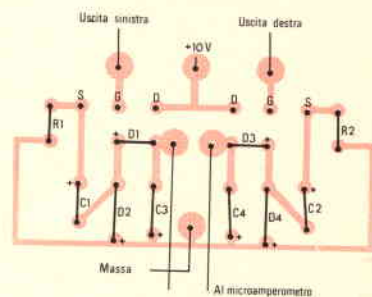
Circuito stampato, visto dal lato componenti, del bilanciatore stereofonico.
